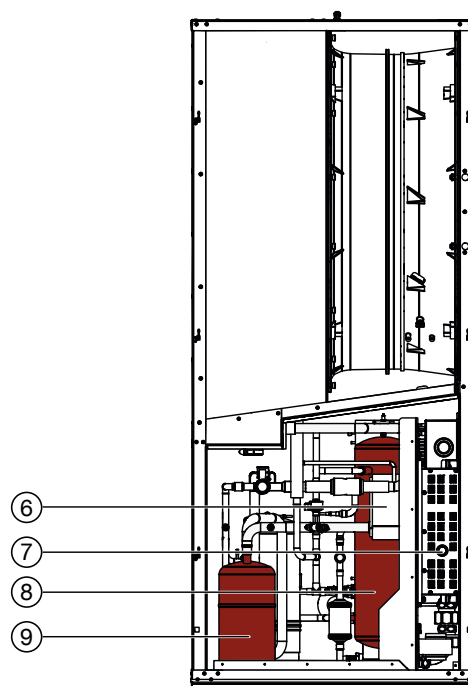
Wärmepumpe Seitenansicht geöffnet
